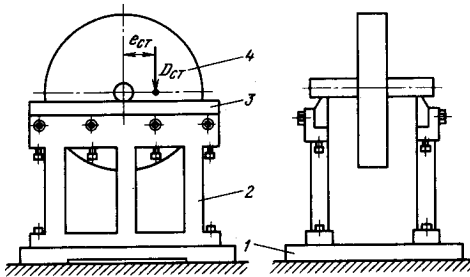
Стенд с горизонтальными параллельными призмами: 1 — основание; 2 — стойки; 3 — призмы различного поперечного сечения; 4 — ротор
